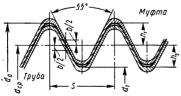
Схема расположения полей допусков на трубную цилиндрическую резьбу
